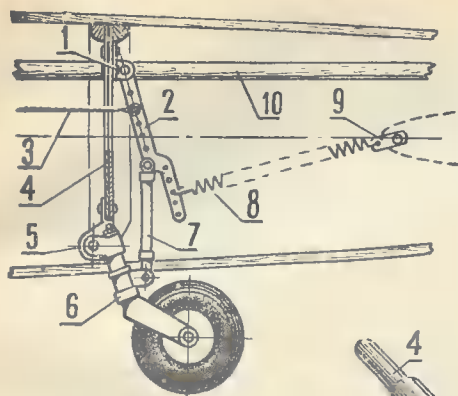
Костыльная установка: 1 — кронштейн; 2 — качалка уборки; 3 — трос; 4 — шпангоут; 5 — кронштейн навески; 7 — амортизатор; 8 — пружина уборки костыля; 9 — узел навески пружины; 10 — тяга руля высоты.
